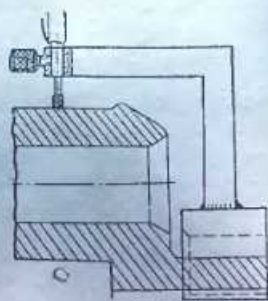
Призма с индикатором для проверки радиуса кривошипа вала
